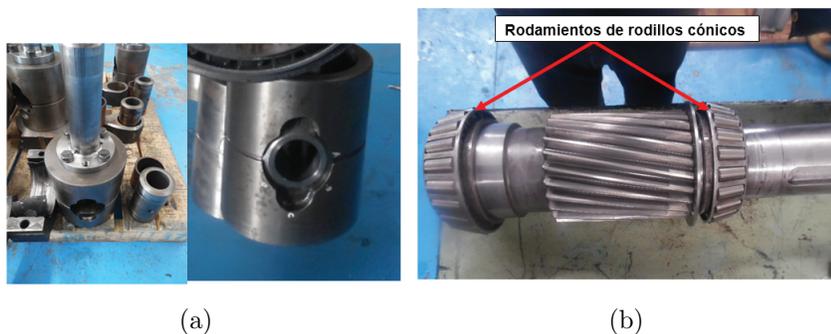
a). Cross head. b) Rodamientos cónicos.
